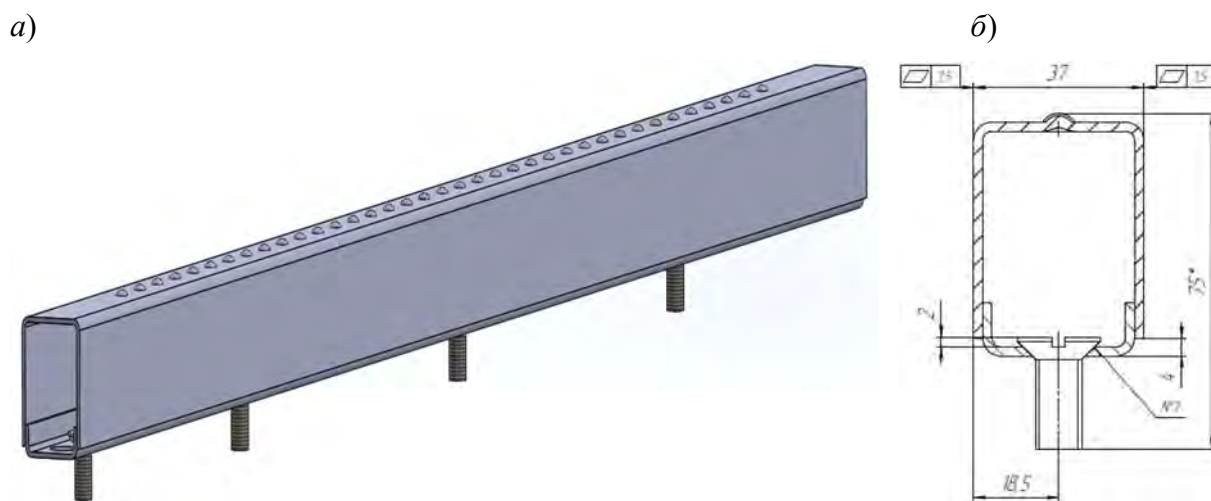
Порог рамы нижней кабины лифта: а – общий вид; б – вид сварного соединения «винт + пластина» в разрезе
